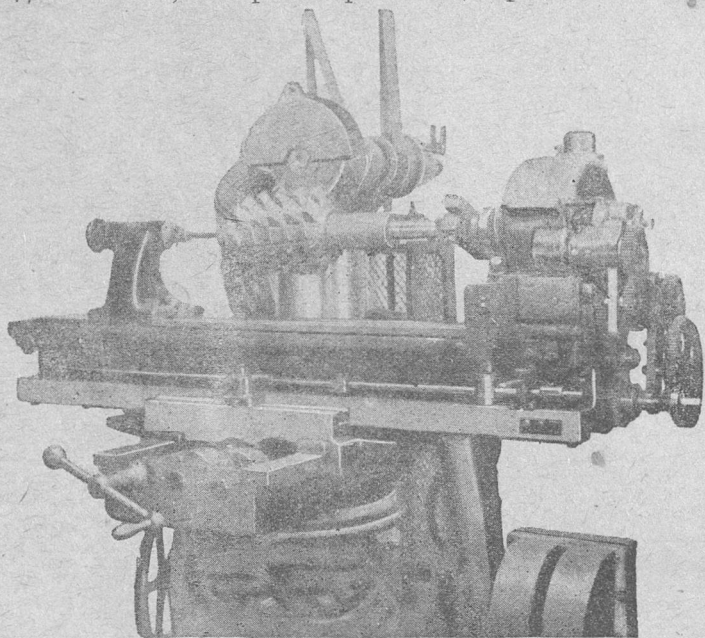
Заточка червячной фрезы на станке Рейнекер.
